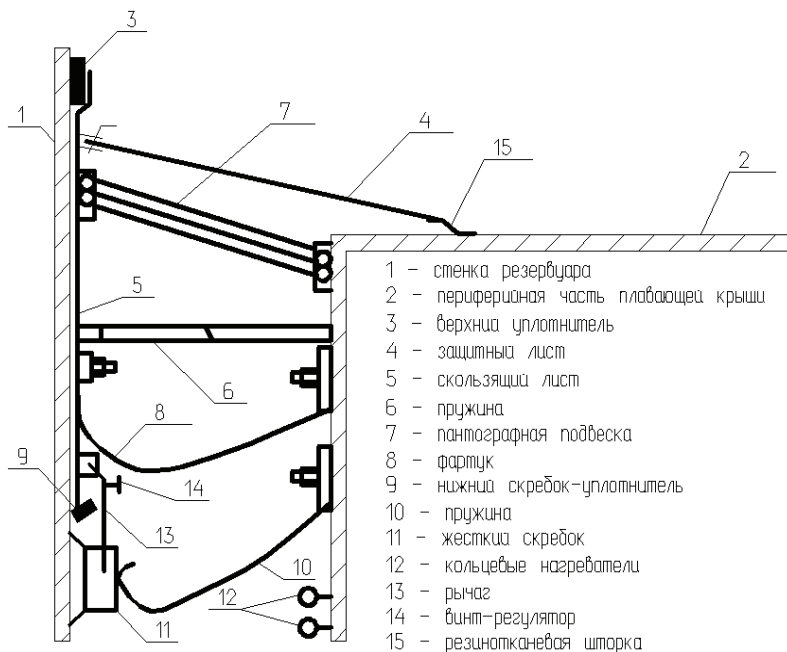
Конструкционная схема уплотняющего затвора плавающей крыши резервуара с шарнирно - стержневой системой.
